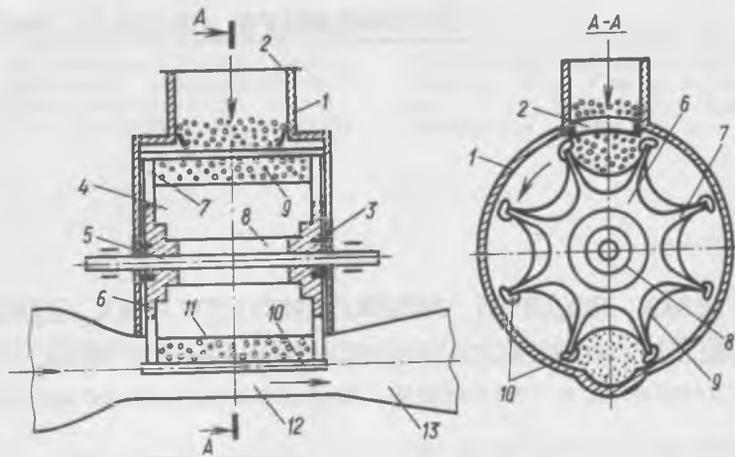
Схема соединения лопастного питателя с трубопроводом:
